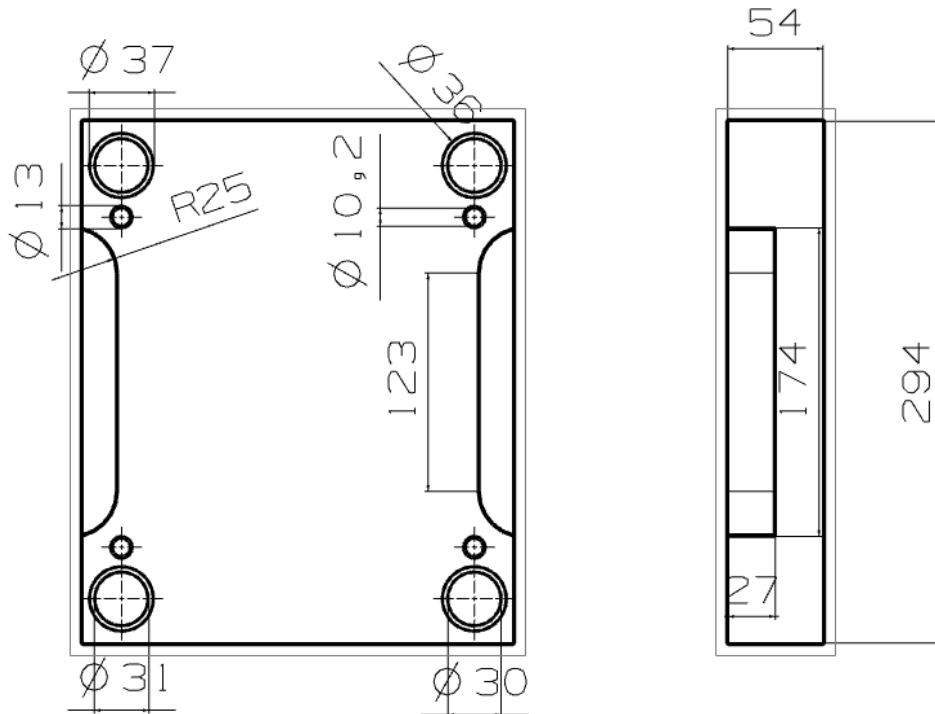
Dimensiones placa frontal de cavidad P1
